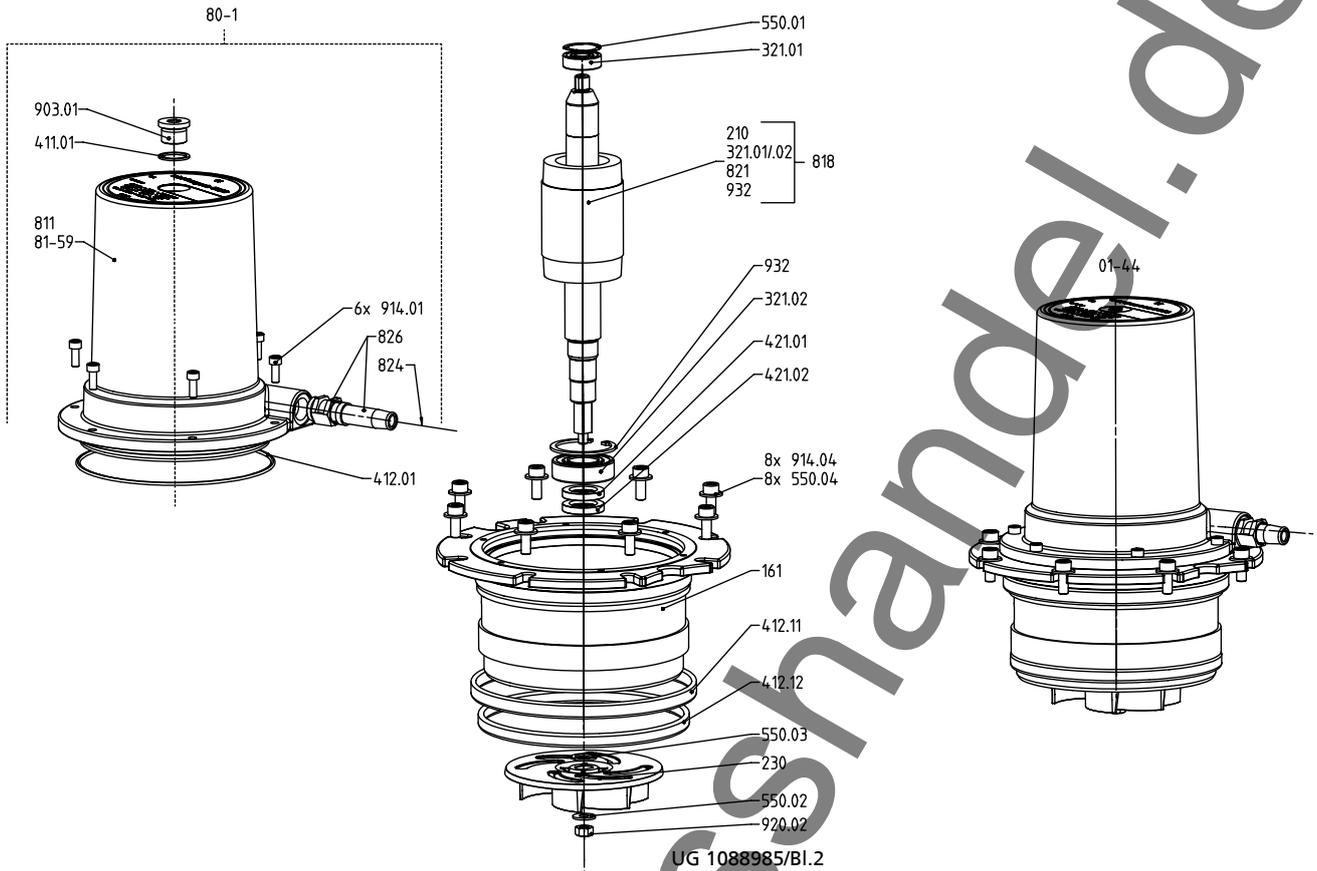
Explosionsdarstellung mini-Compacta U60, U100 - Laufteil
